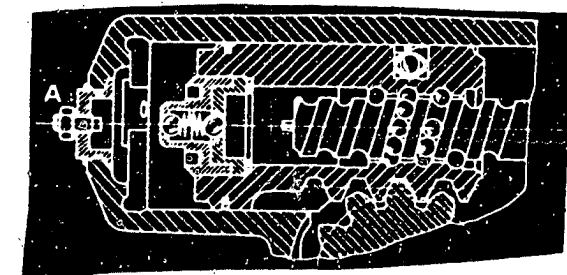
Schnitt durch das Lenkgetriebe. A zeigt auf die Einstellschraube des Begrenzungsventils.
